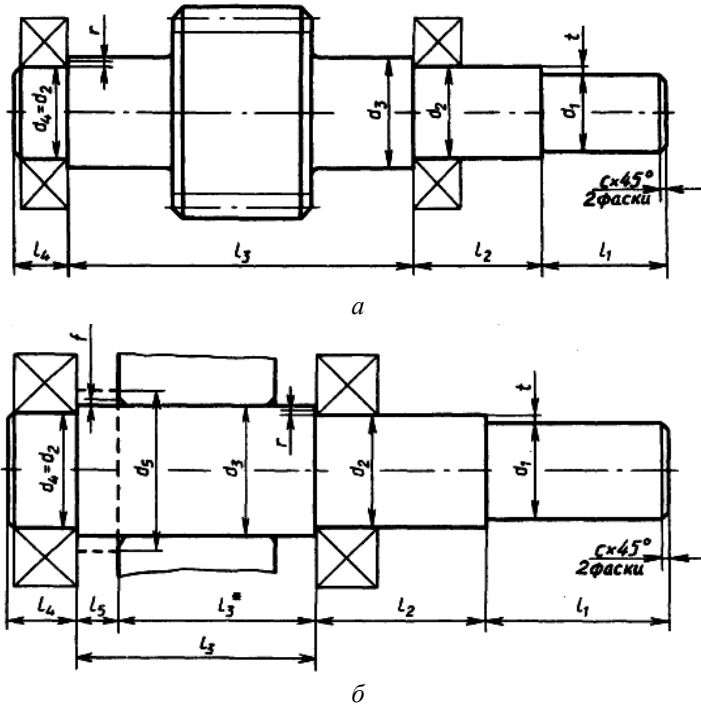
Типовые конструкции валов одноступенчатых цилиндрических редукторов: а – вал шестерня; б – вал колеса.
